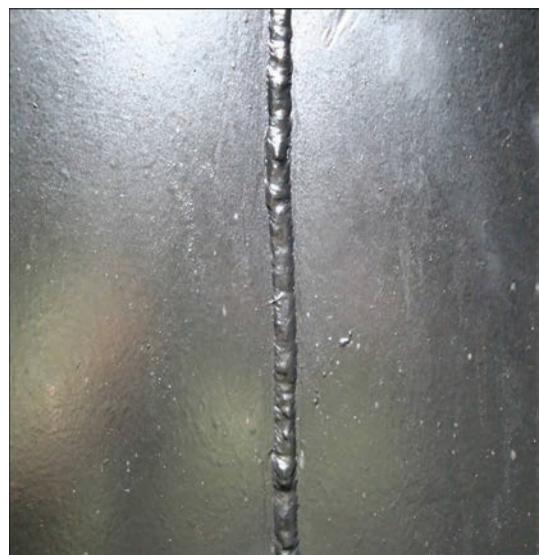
Общий вид вертикальных сварных швов на внутренней поверхности стенки основного резервуара
